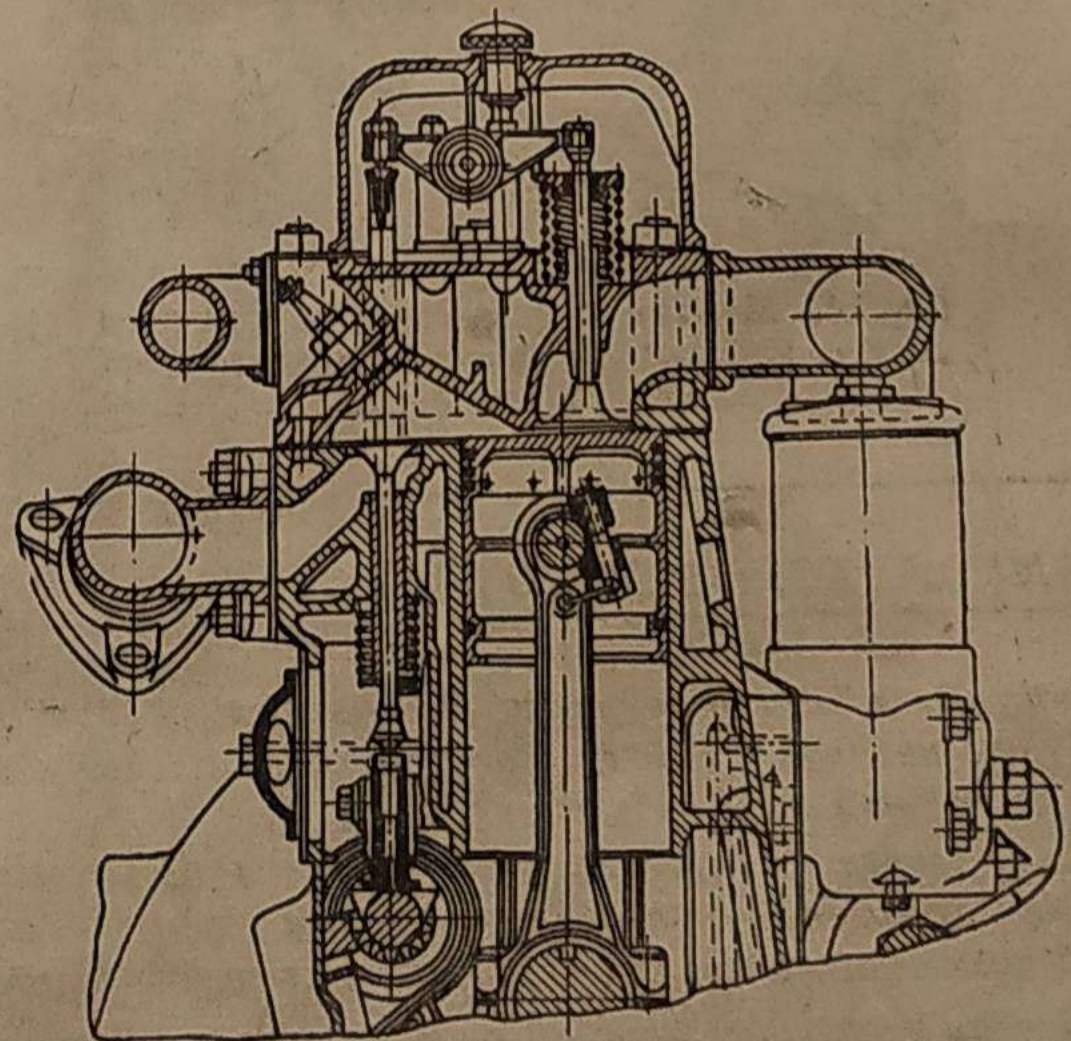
Поперечный разрез двигателя ЗИС-5 с головкой блока НАТИ-ВК.
